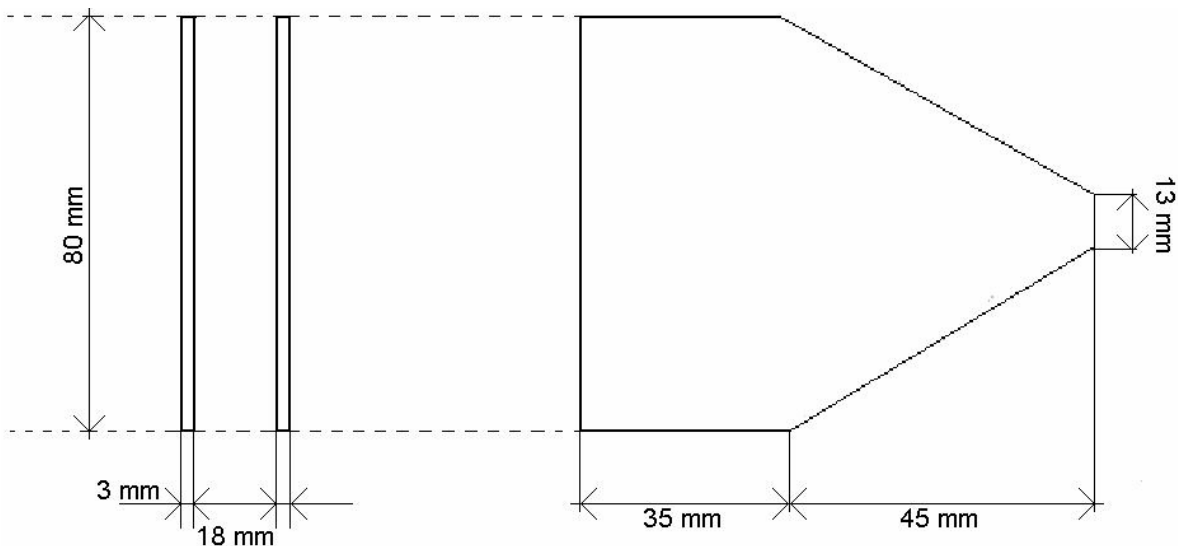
Dimensiones del módulo. A la izquierda la vista frontal, a la derecha la vista lateral.
